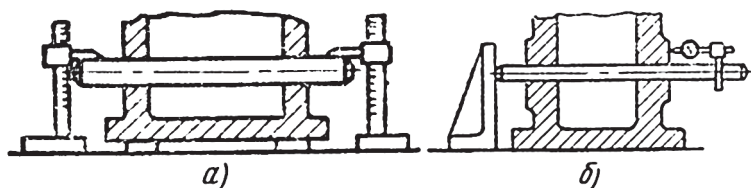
Схема проверки точности расположения отверстий в корпусе червячного редуктора:
